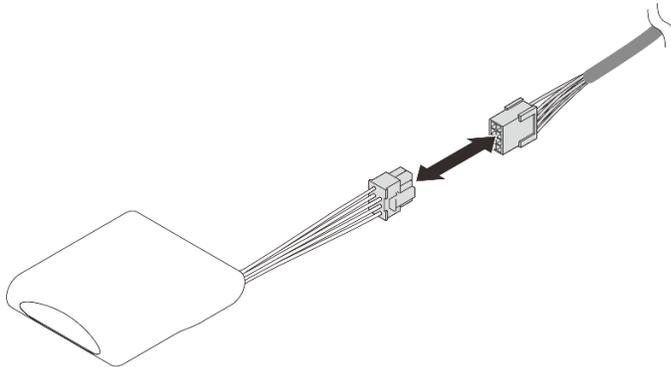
Collegamento del cavo del modulo di alimentazione Flash
